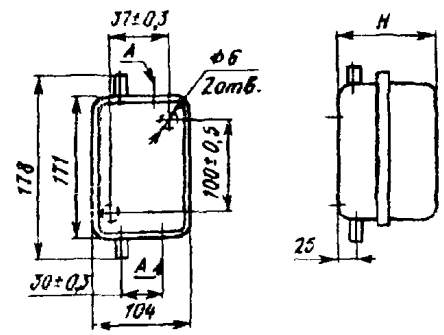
Габаритные, установочные размеры пускателей типа ПМ12-010 нереверсивных в оболочках степени защиты IP54
